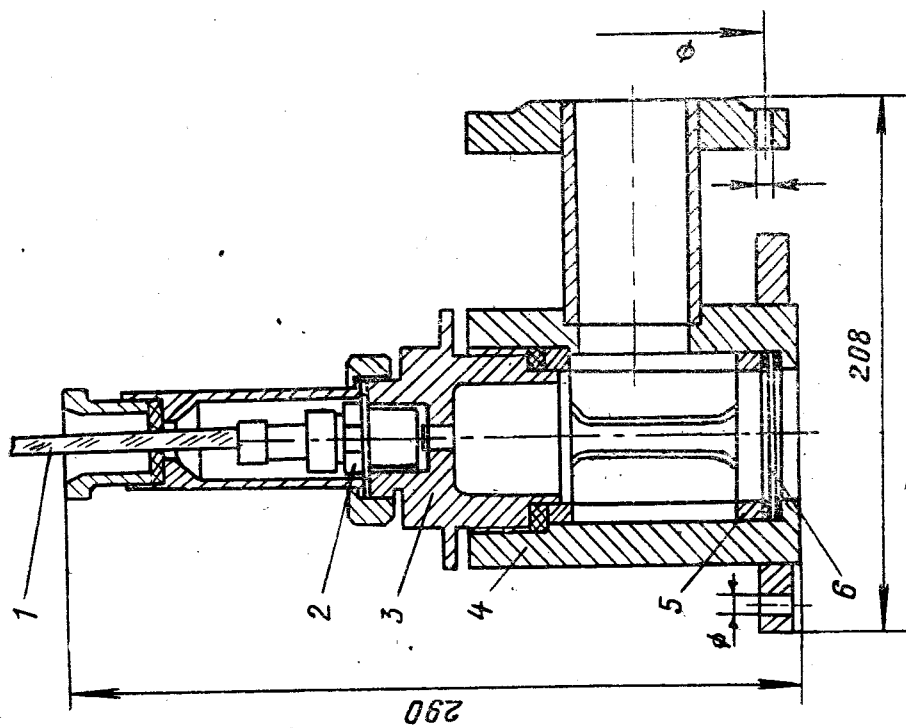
Гидропневмоклапан ГПК-50 (черт. 60463-00.000, п/я А-7210);
